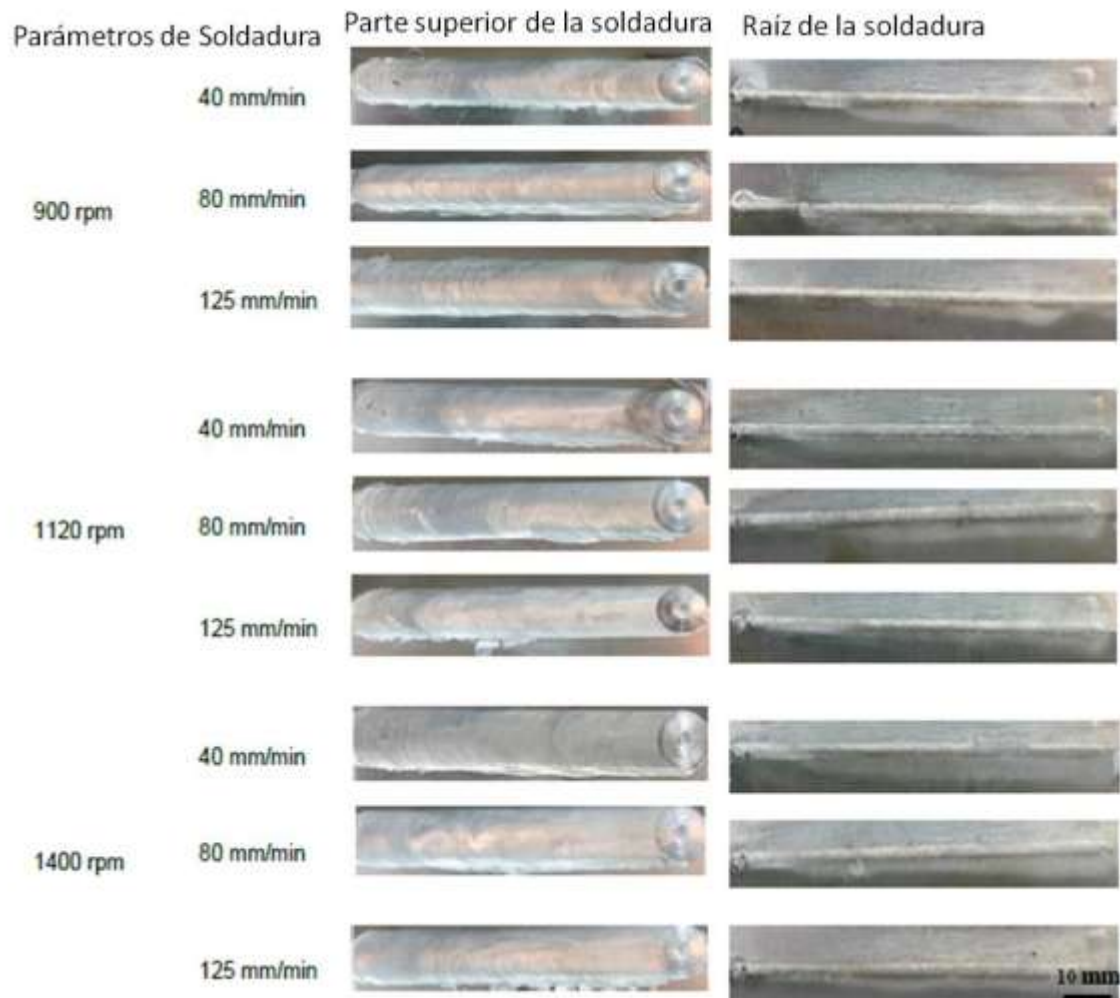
Superficie y raíz de la unión después del proceso de soldadura por fricción. ⁽³³⁾
